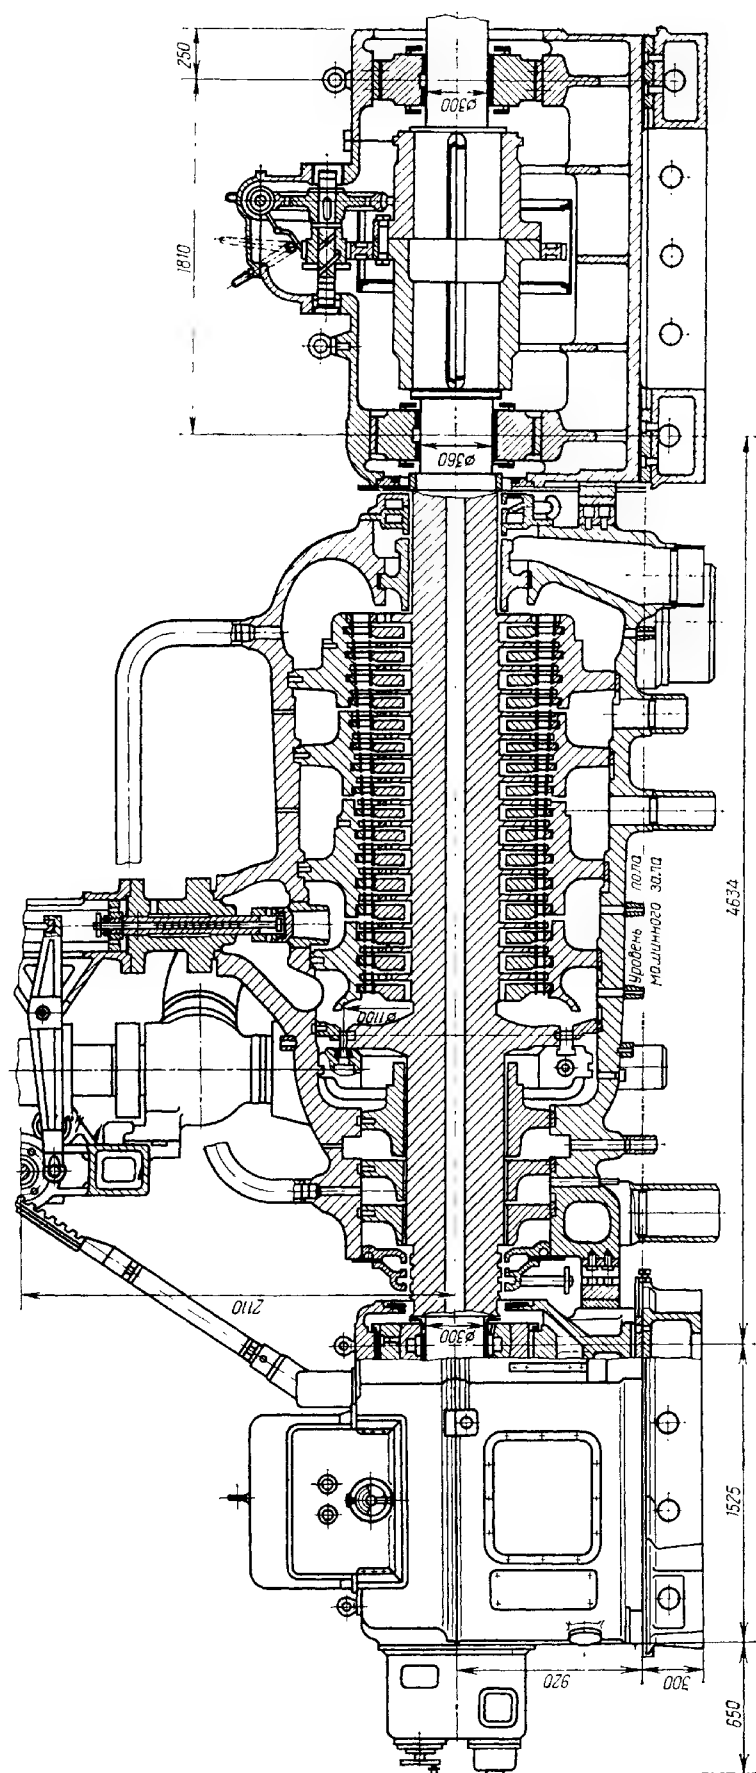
Продольный разрез паровой турбины Р-50/60-130/13
